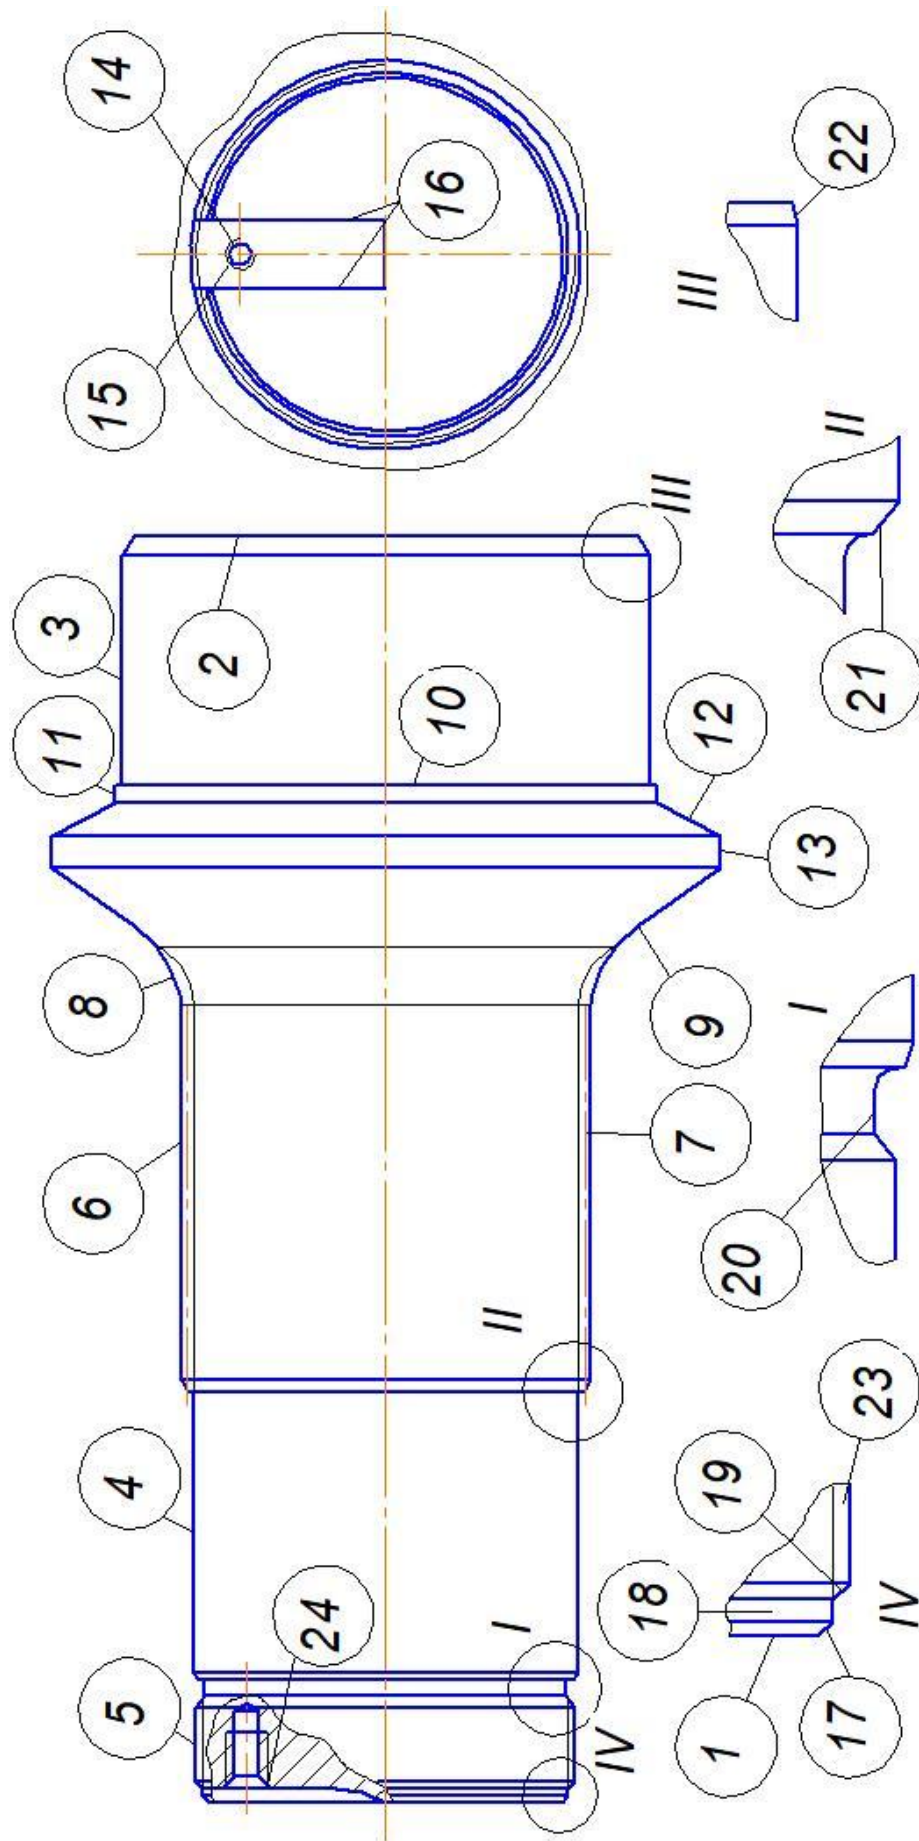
Ескіз хвостовика з номерами поверхонь
